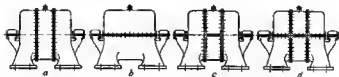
Esquemas de la separación del cuerpo de una máquina de rotor
